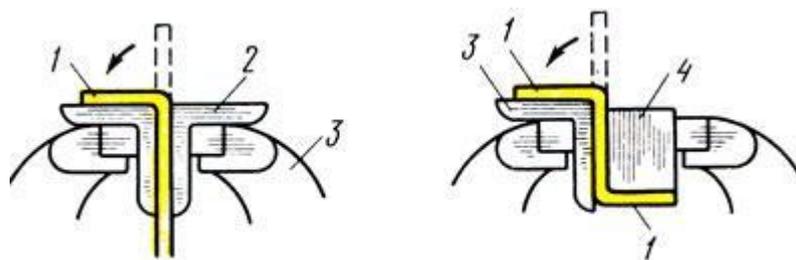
Гибка двойного угольника: 1 - заготовка, 2 - нагубники, 3 - тиски, 4 - брусок-подкладка
